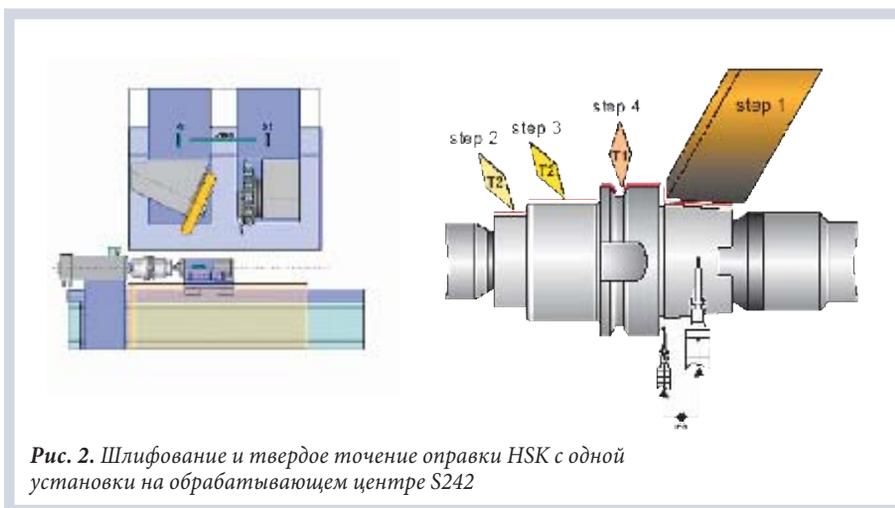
Шлифование и твердое точение оправки HSK с одной установки на обрабатывающем центре S242
